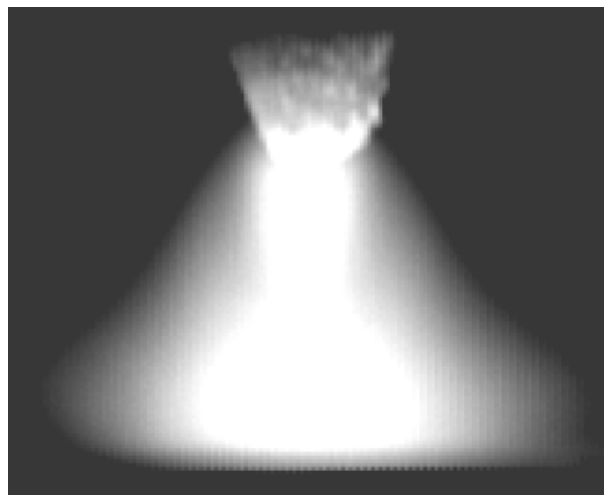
imagem do arco elétrico formado pela solda TIG.
